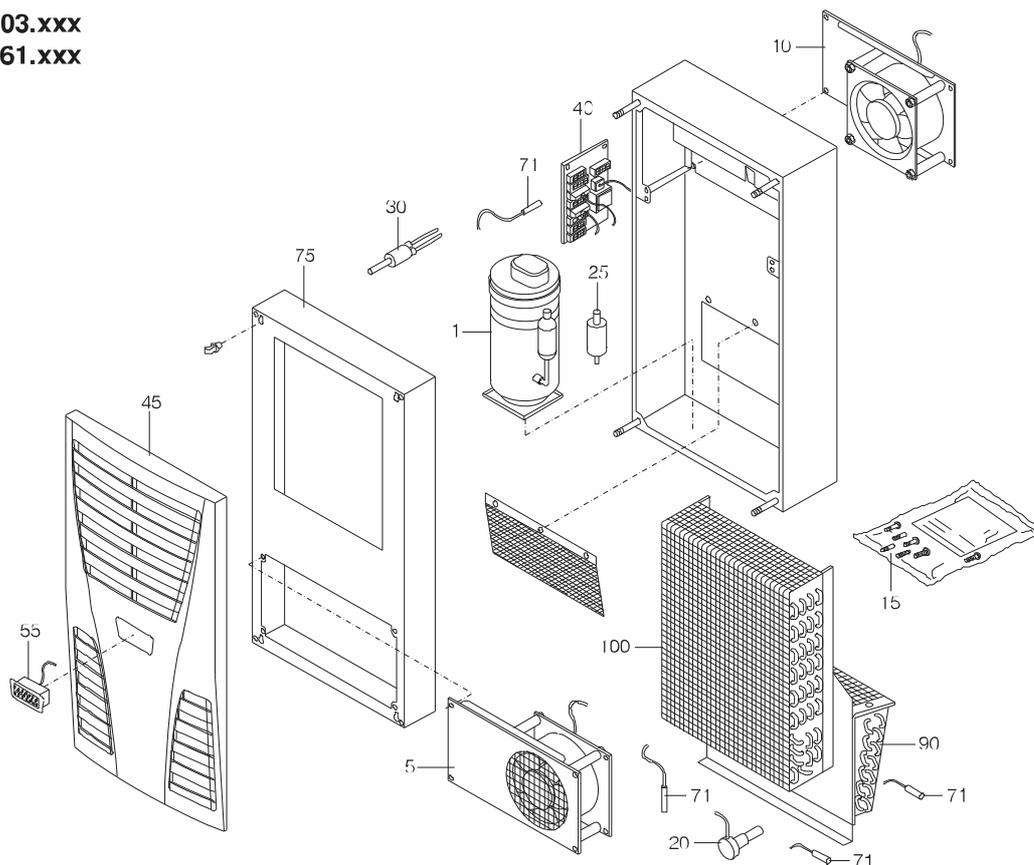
Pièces de rechange pour SK 3303.xxx, SK 3361.xxx
